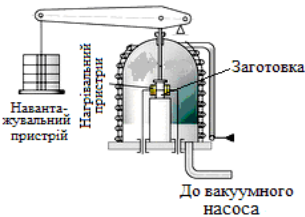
Схема дифузійного зварювання у вакуумі
